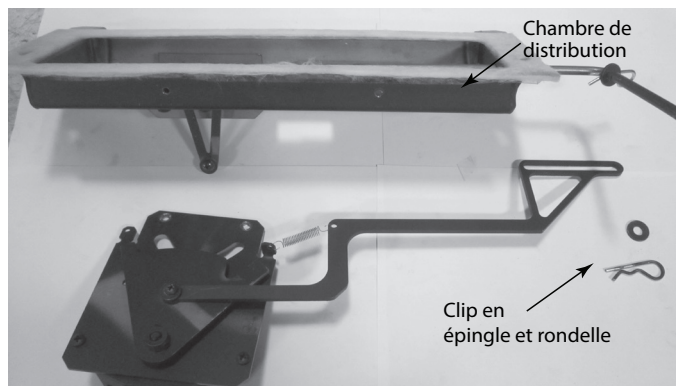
Retrait du clip en épingle à cheveux, de la rondelle et de la chambre à air.
